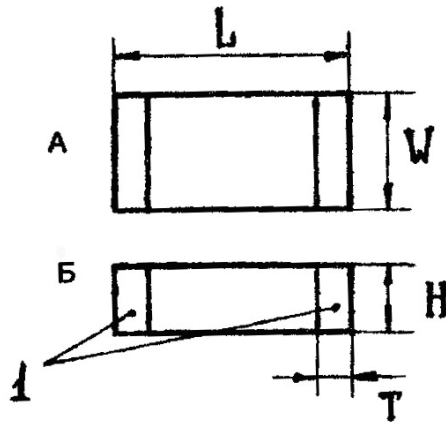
Корпус прямокутної форми (Chip-корпус) (А. Вид зверху. Б. Вид збоку. 1. Виводи)
